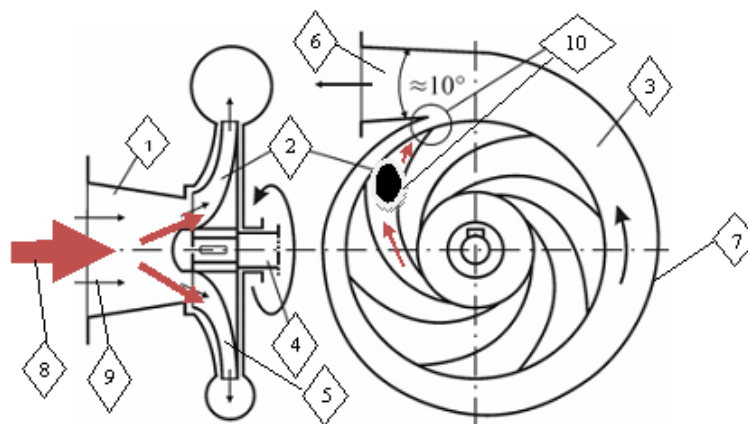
Схема попадания камней в полость пожарного насоса: 1 - всасывающий патрубок, 2 - камень, 3 - спиральная камера, 4 - вал насоса, 5 - рабочее колесо, 6 - напорный патрубок, 7 - корпус насоса; 8 - направление движения камня; 9 - направление движения жидкости; 10 - вероятное место остановки камней
